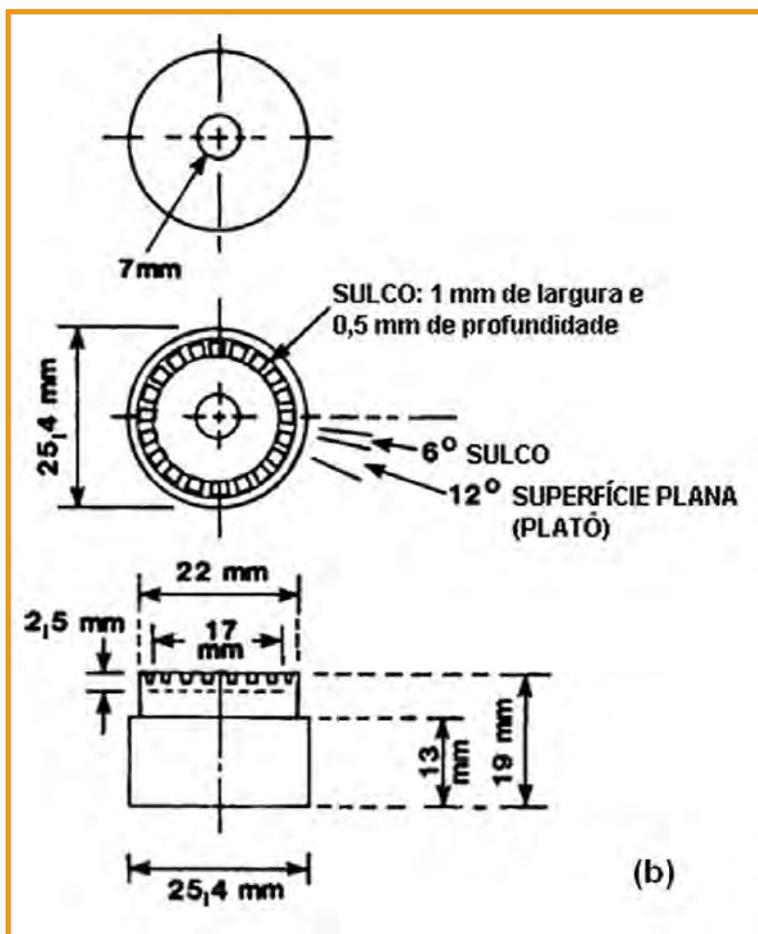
(b) Detalhes do dispositivo formador de frestas (arruela segmentada)
